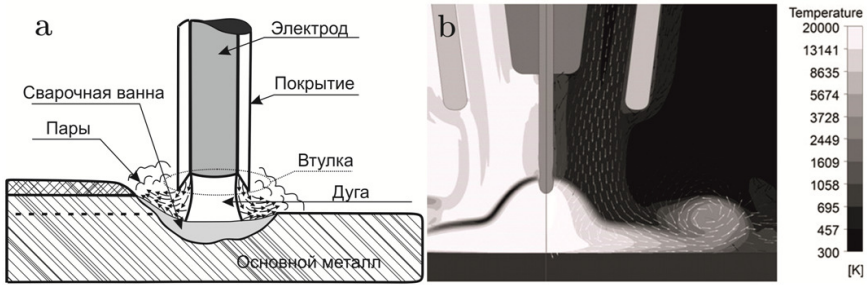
Схема сварки штучным электродом (а) и компьютерное моделирование [9] сварки в защитном газе (б)
